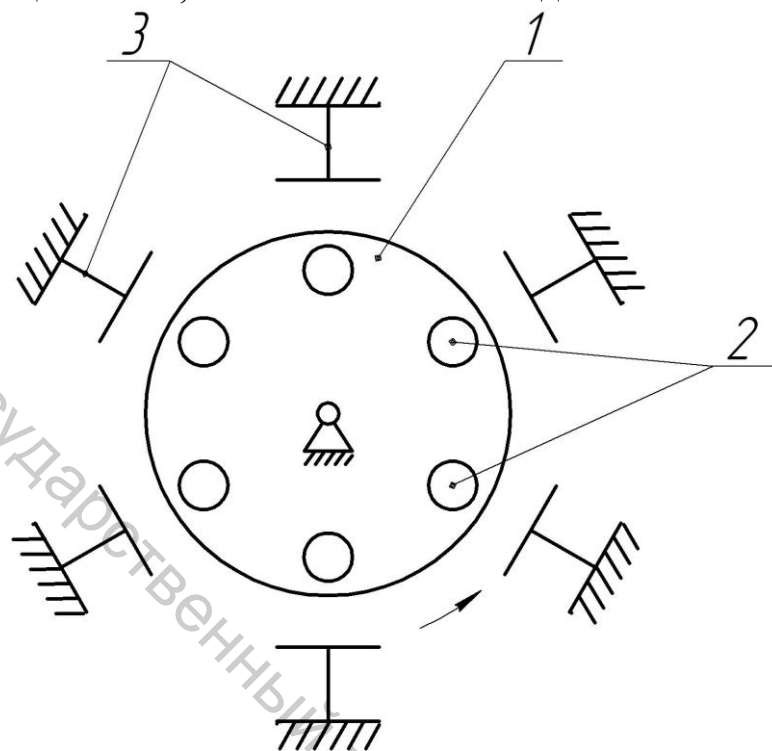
Схема многопозиционной роторной машины-автомата: 1 – транспортирующий ротор, 2 – обрабатываемые детали, 3 – рабочие инструменты
